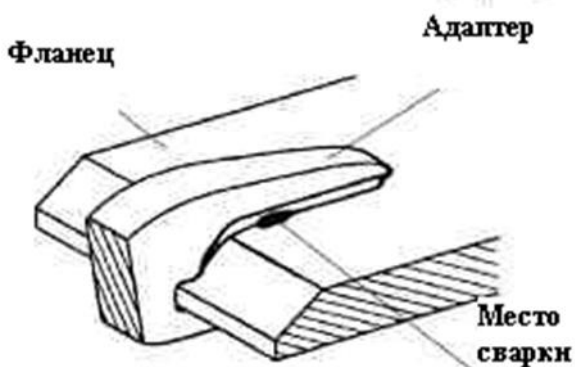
Схема сварки адаптера к режущей кромке ковша
